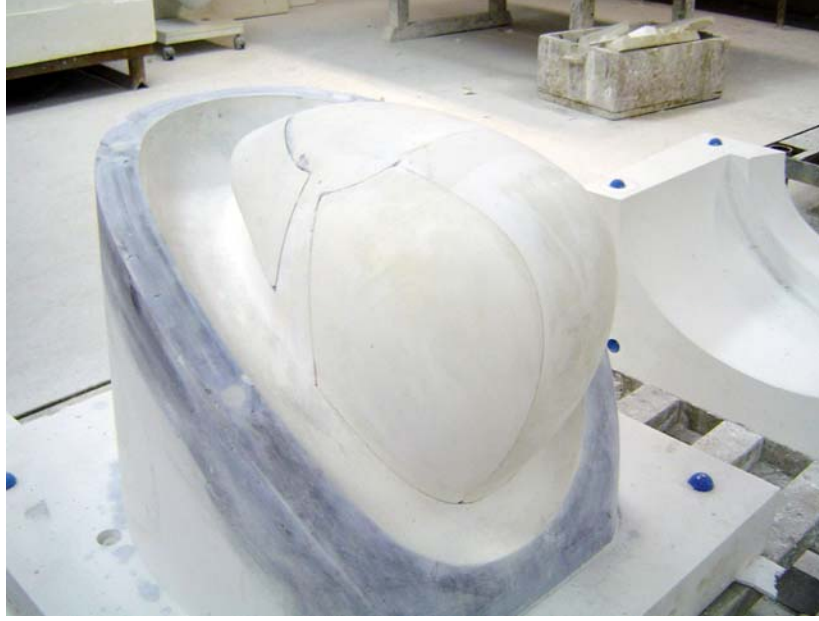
Yan ve üst parçaların alıştırma sonrası görünümü
